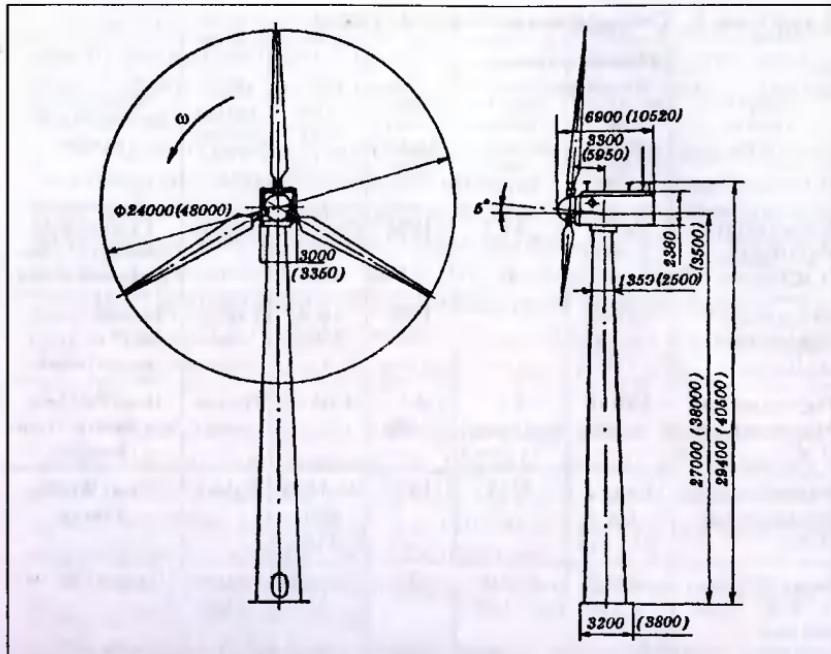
Общий вид и основные размеры ВЭУ типов Р-250 и Р-1000
